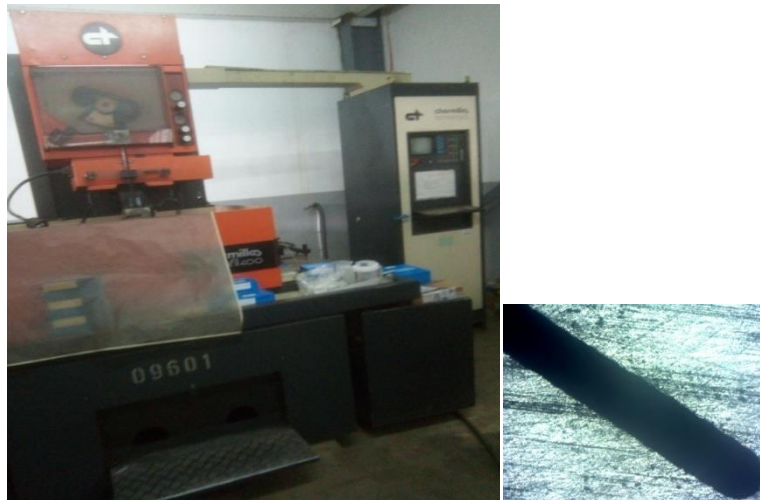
Machine d'usinage par électro-érosion à fil à commande numérique CHARMILLES - Type : ROBOFIL 400 FMO FRANCE MACHINES-OUTILS
